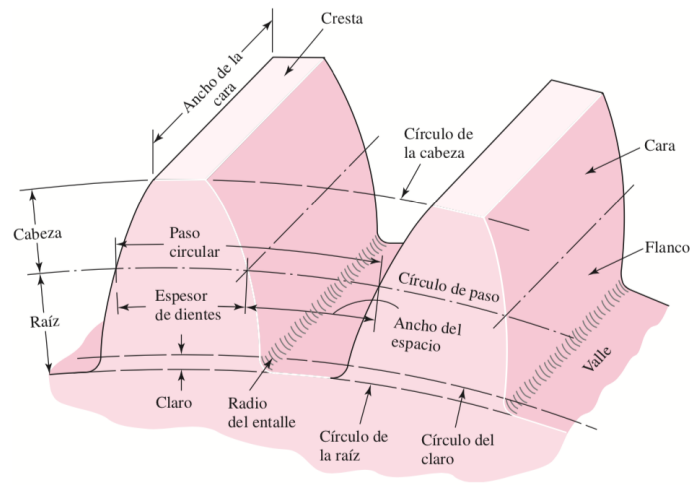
Nomenclatura que presentan los engranajes rectos. Fuente: [14].
